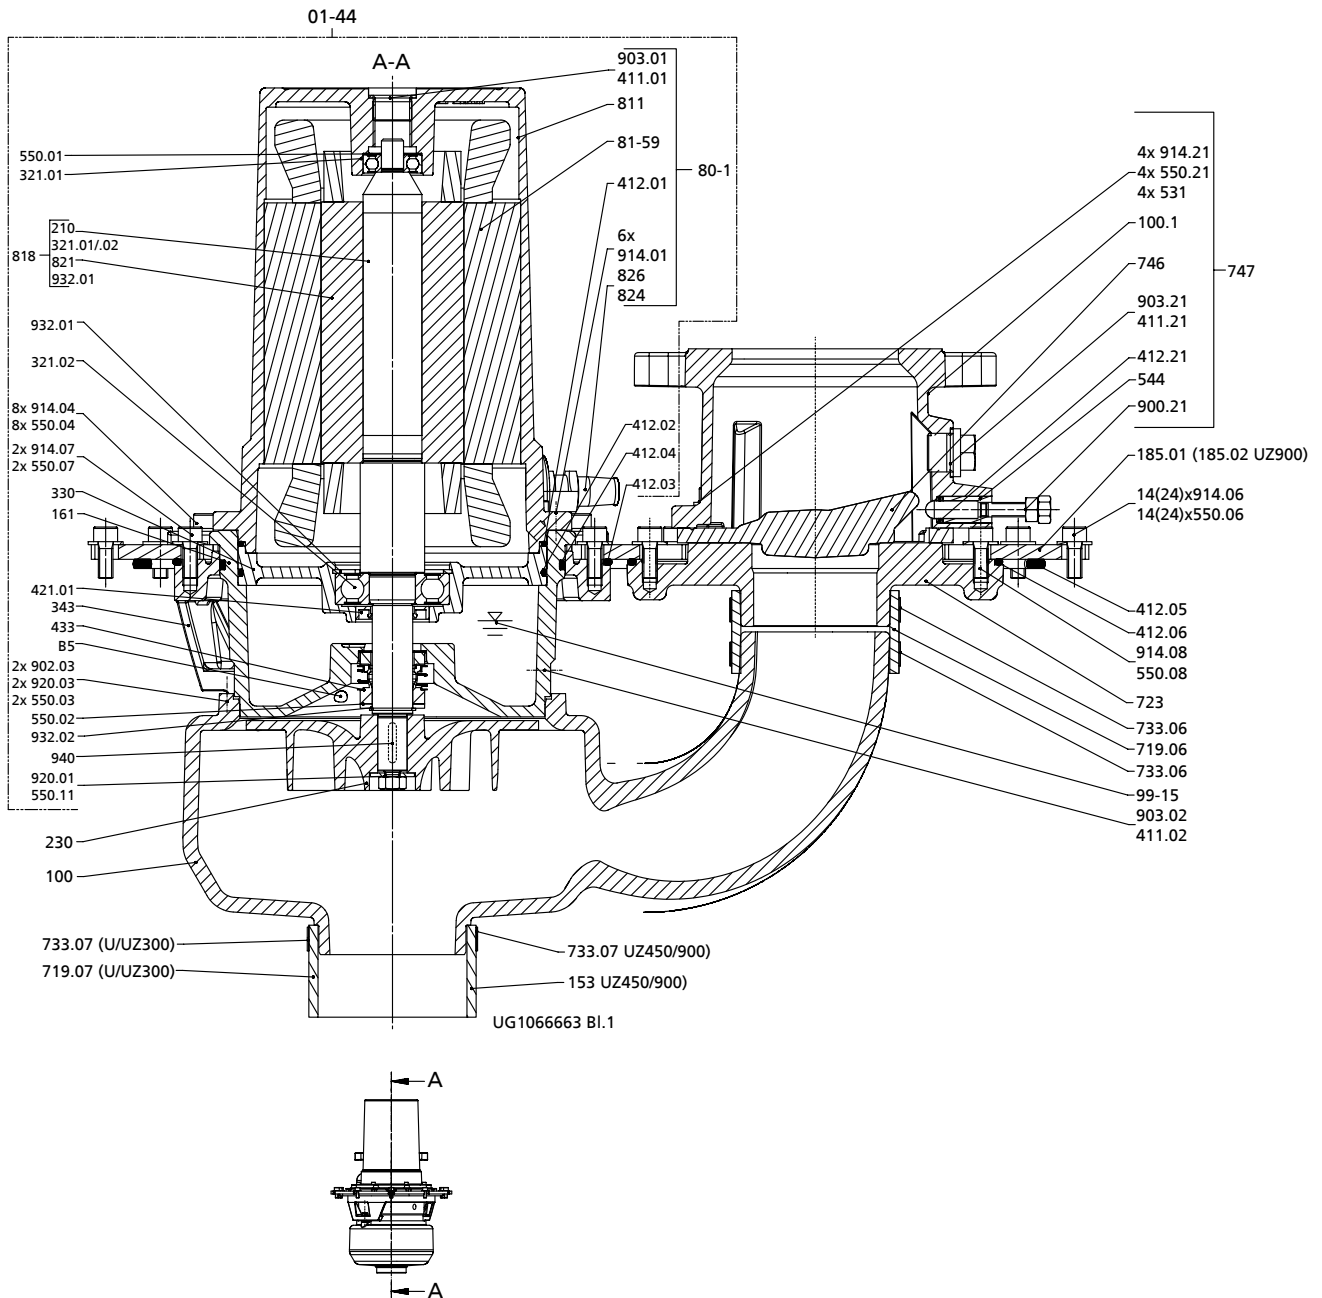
Сборочный чертеж Compacta U100/300, UZ150/300, UZ 450/900 — съемный узел
